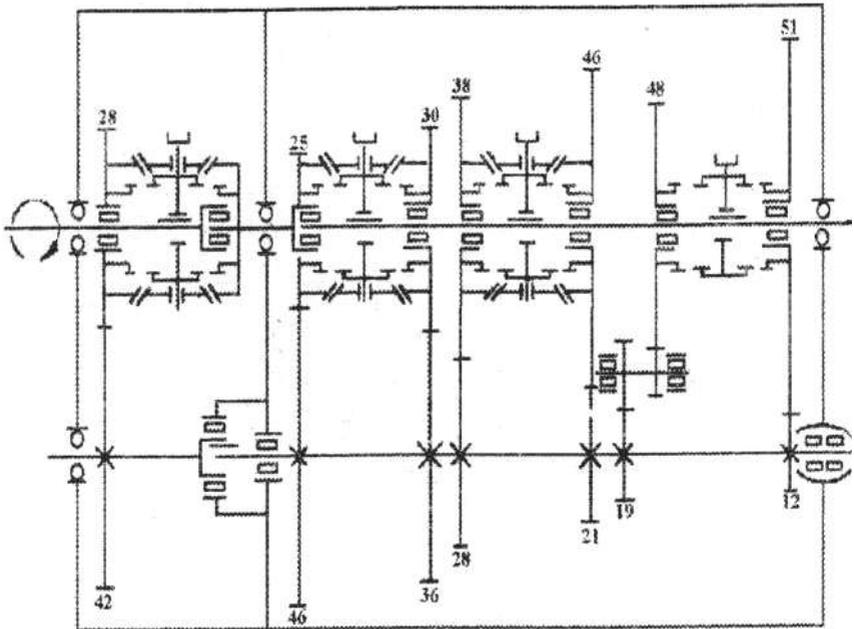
Кінематична схема коробки передач автомобіля КАМАЗ-5320
